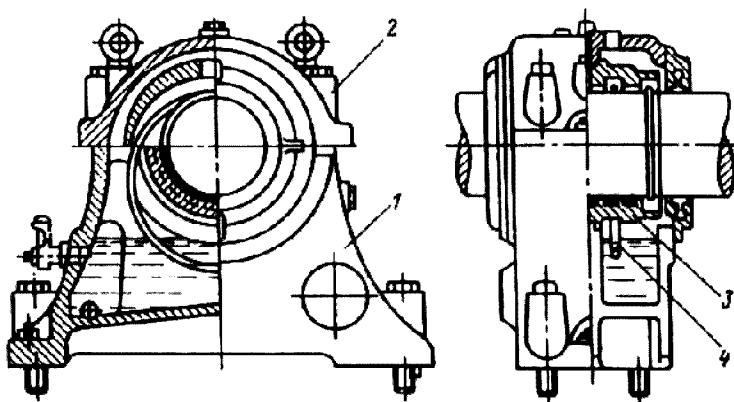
Стояковый подшипник с кольцевой смазкой
